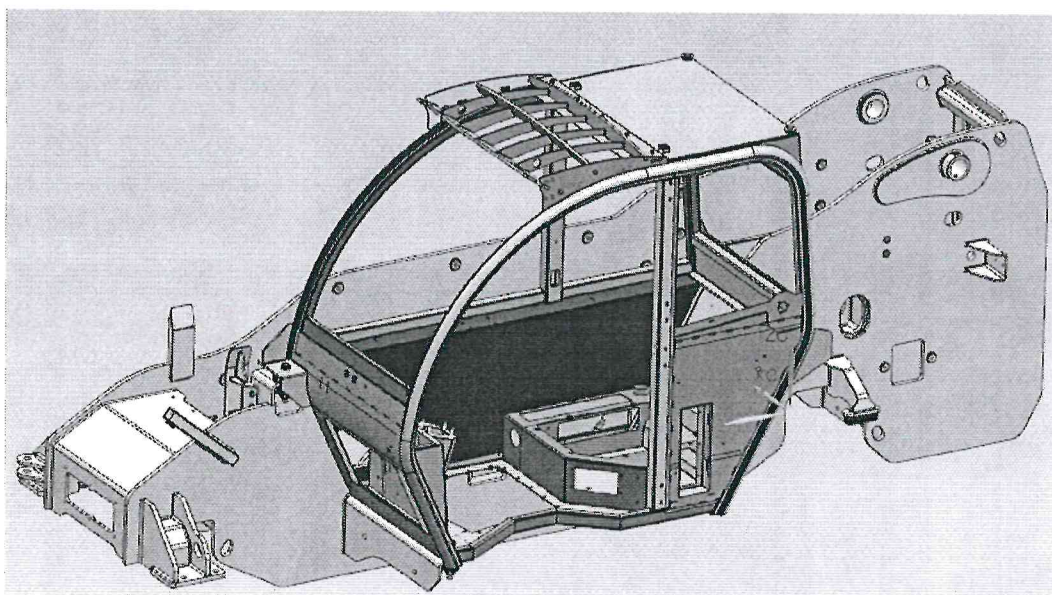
3D модель каркаса кабины с рамой (взамен рамы допускается изготовление станда с конструкцией, способом крепления и местами расположения кронштейнов крепления кабины к станду аналогичными раме погрузчика).
